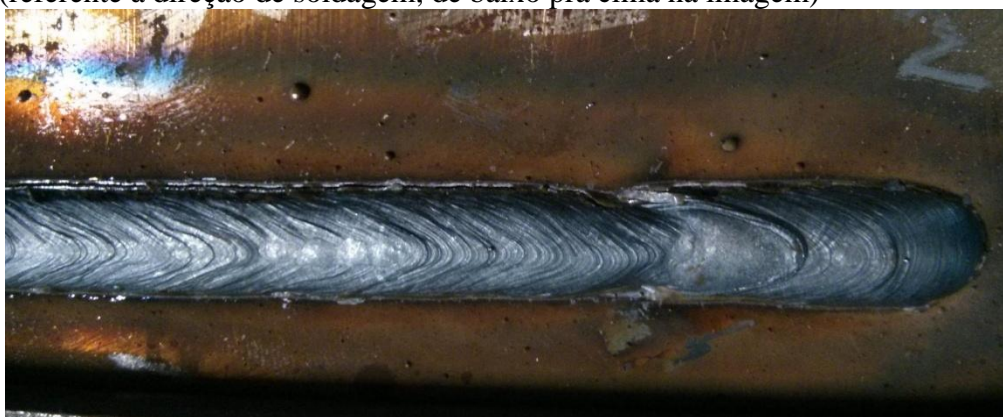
Experimento M2 mostrando a trinca na região marginal direita da solda (referente à direção de soldagem, lado superior da imagem).
